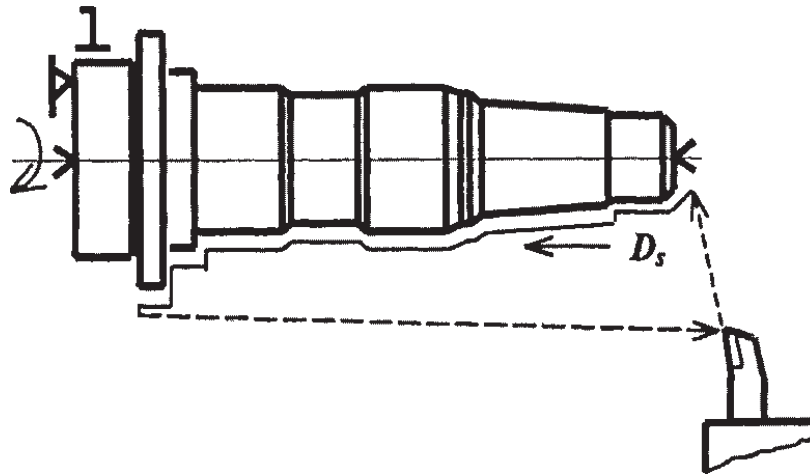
Схема обработки наружных поверхностей на токарном станке с ЧПУ
